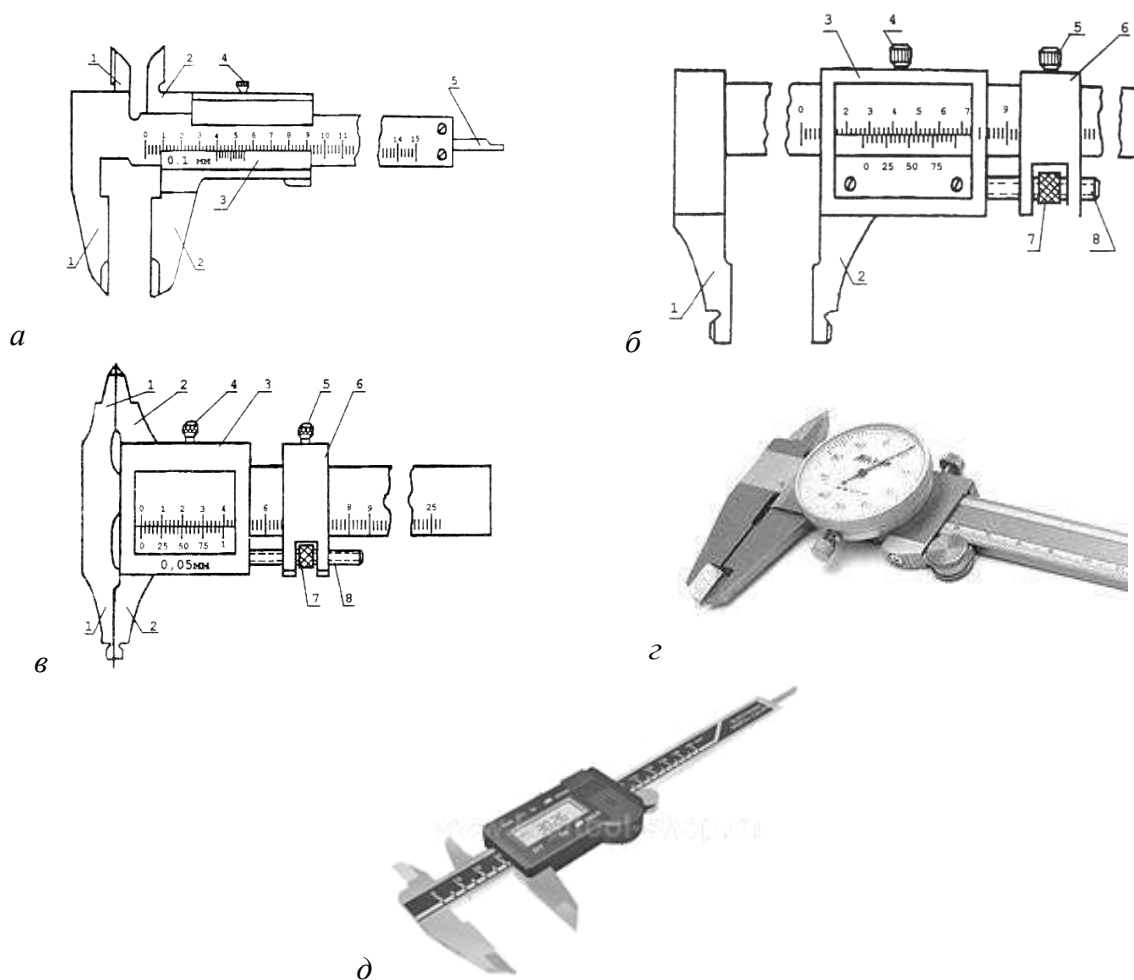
Типы штангенциркулей: *a* – ШЦ-I; *б* – ШЦ-II;
